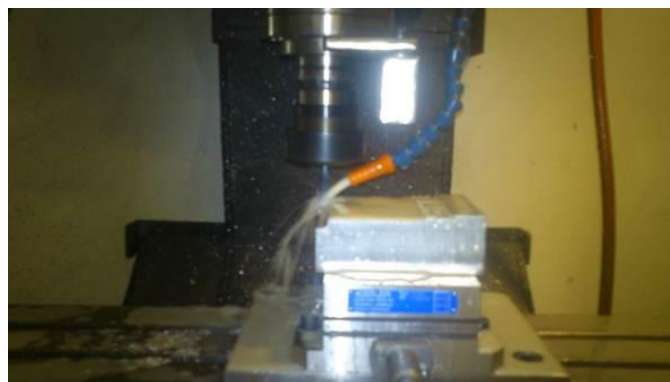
Fresagem de topo com fresa hemisférica do alumínio
